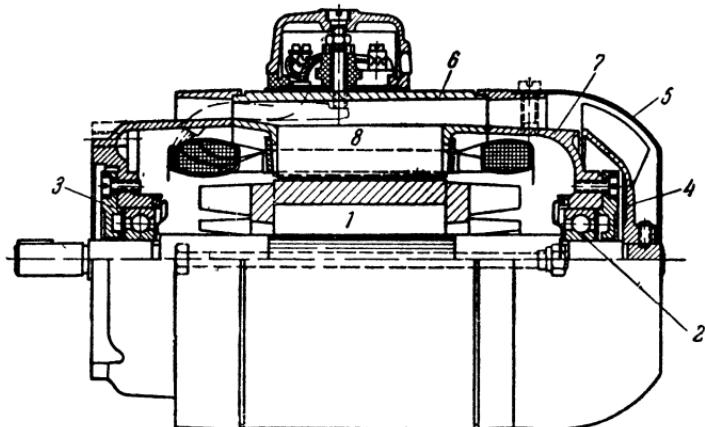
Асинхронный двигатель заводского изготовления.
